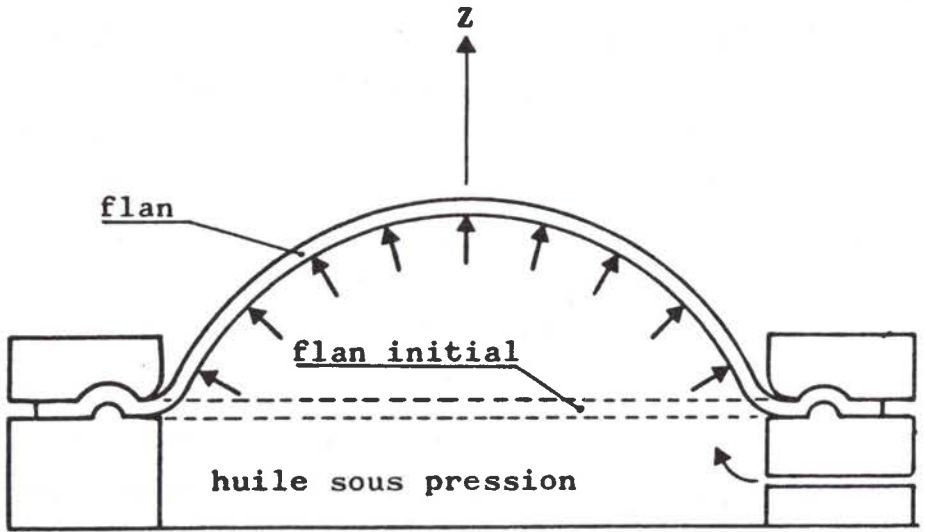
/3 Essai Jovignot de gonflement hydraulique -
